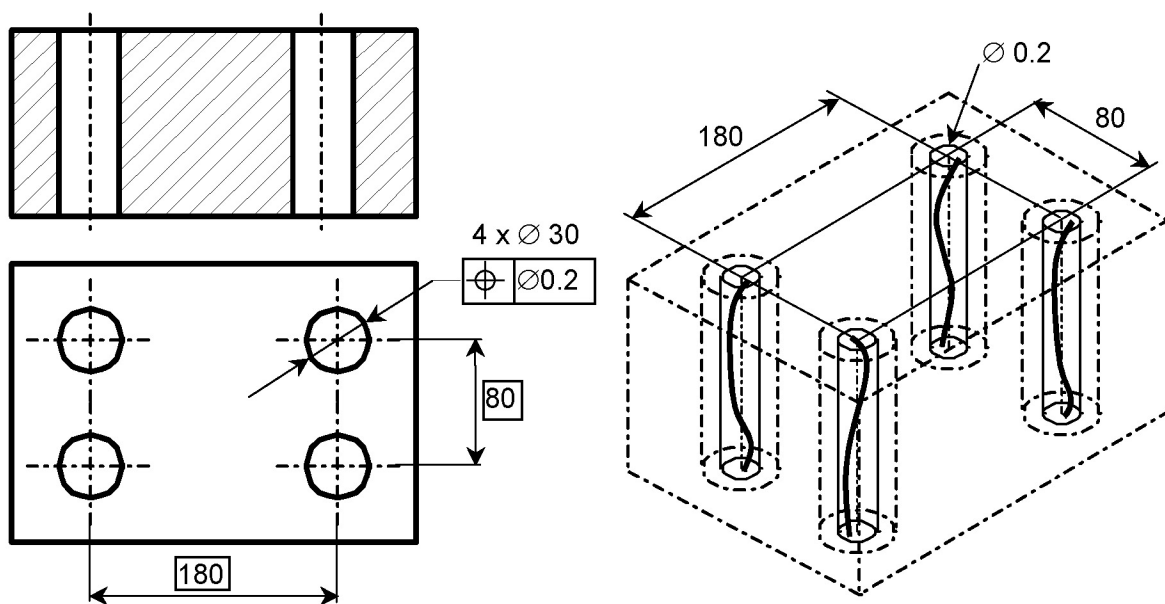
Tolerancia de posición para los ejes de cuatro elementos con zona de tolerancia cilíndrica
